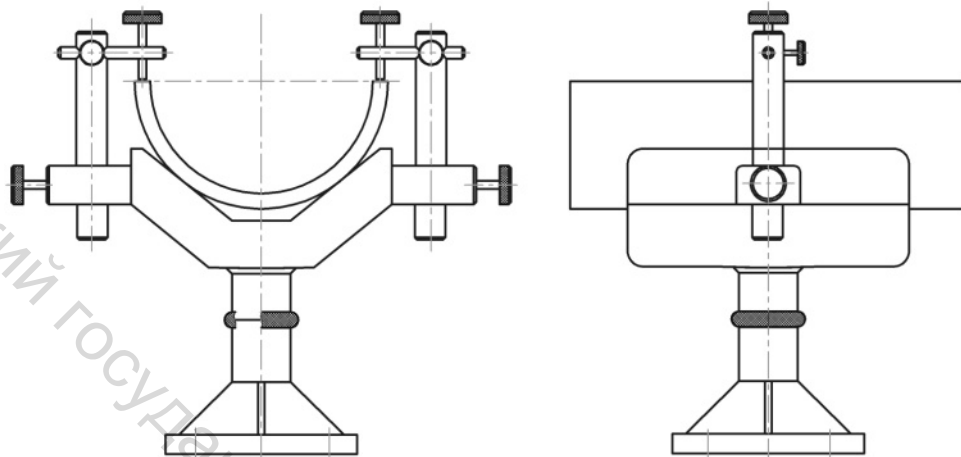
Приспособление для зажатия вкладышей подшипников при шабрении
